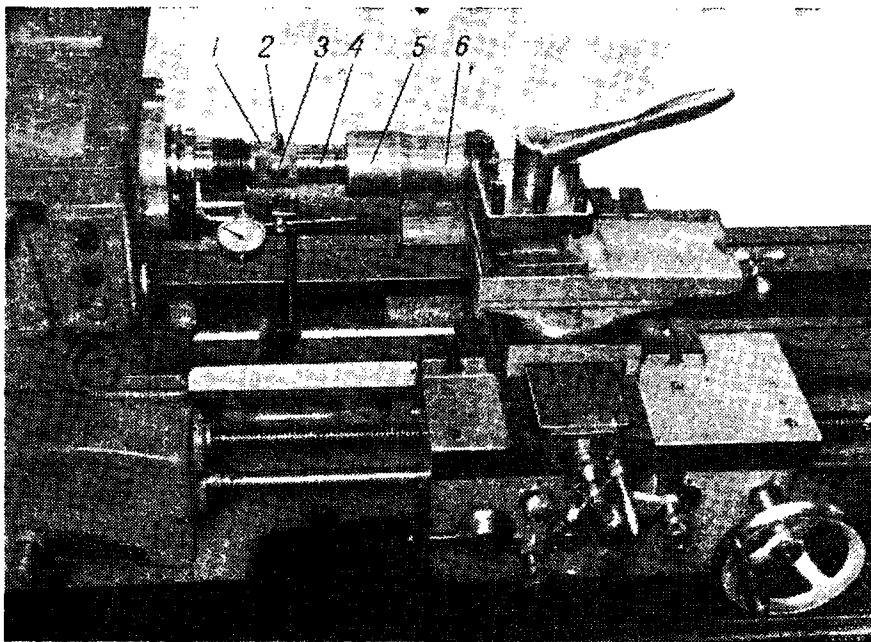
Проверка зазоров и жесткости узла шпинделя токарного станка в осевом направлении
